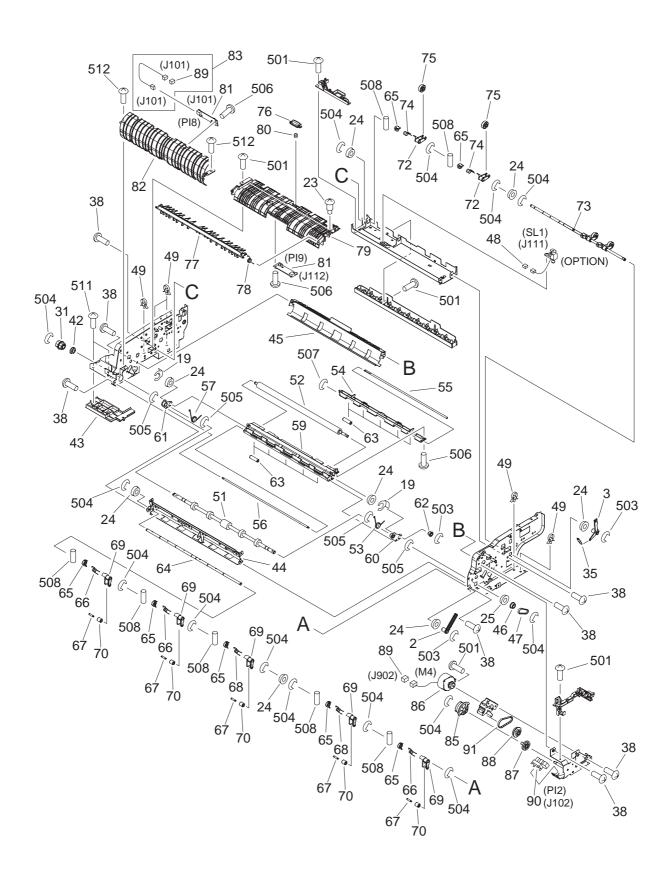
(2/3) PAPER FEEDER ASSEMBLY 搬送部
